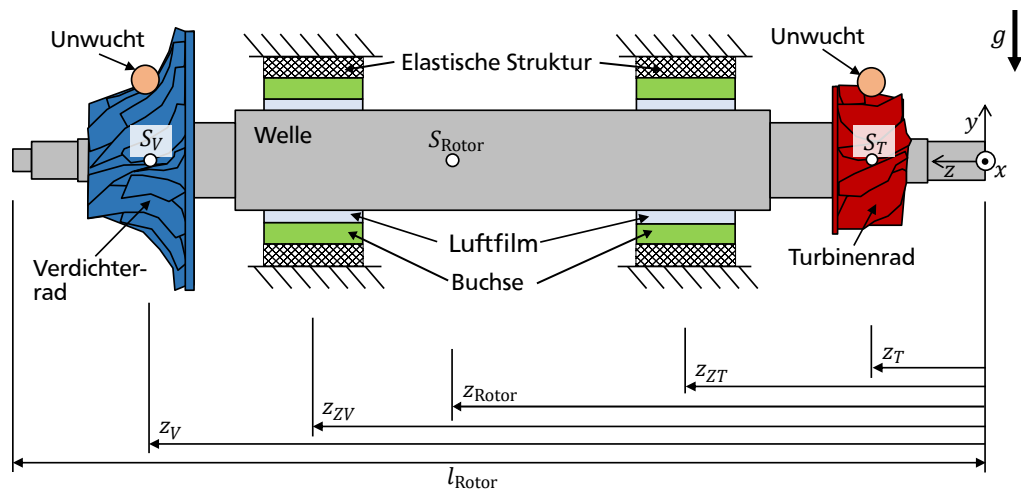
Übersicht des Rotorsystems mit Air Ring Bearings [1–3].
